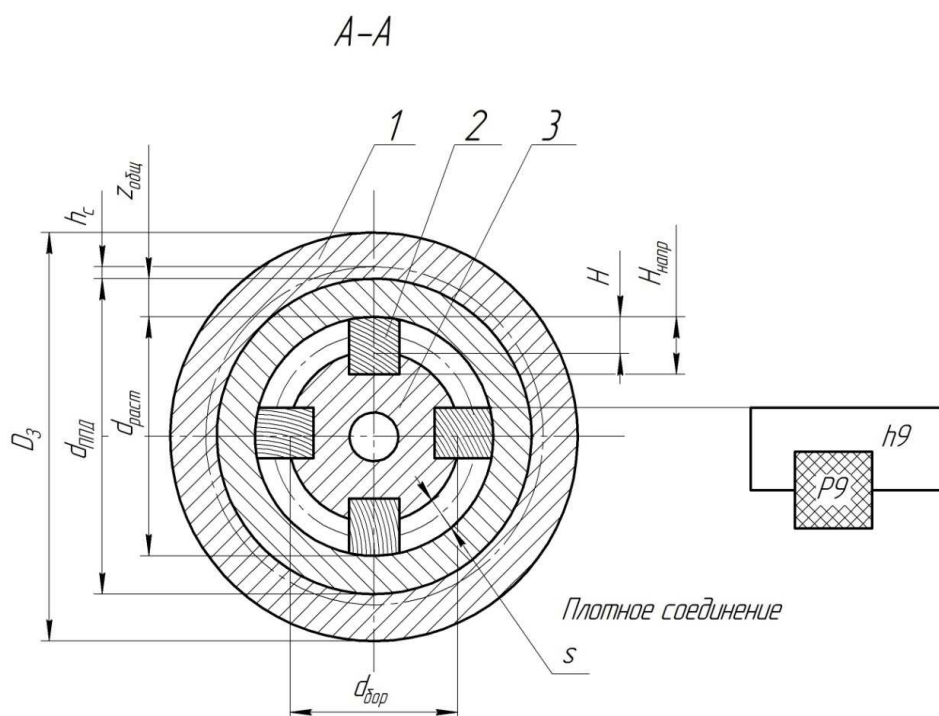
Схема съема общего припуска: 1 – трубная заготовка; 2 – деревянная направляющая; 3 – расточная борштанга; D_3 – наружный диаметр заготовки; $d_{нпд}$ – диаметр ГО, образованный в процессе резания расточным резцом борштанги при съеме большого припуска с образованием поверхностной пластической деформации; h_c – глубина полезного слоя при осуществлении ППД; $z_{общ}$ – общий припуск на растачивание ГО; $d_{раст}$ – диаметр растачивания ГО; $d_{бор}$ – диаметр борштанг; S – зазор между расточной борштангой 3 и заготовкой трубы 1; $H_{напр}$ – общая высота деревянной направляющей; H – выступающая часть деревянной направляющей
